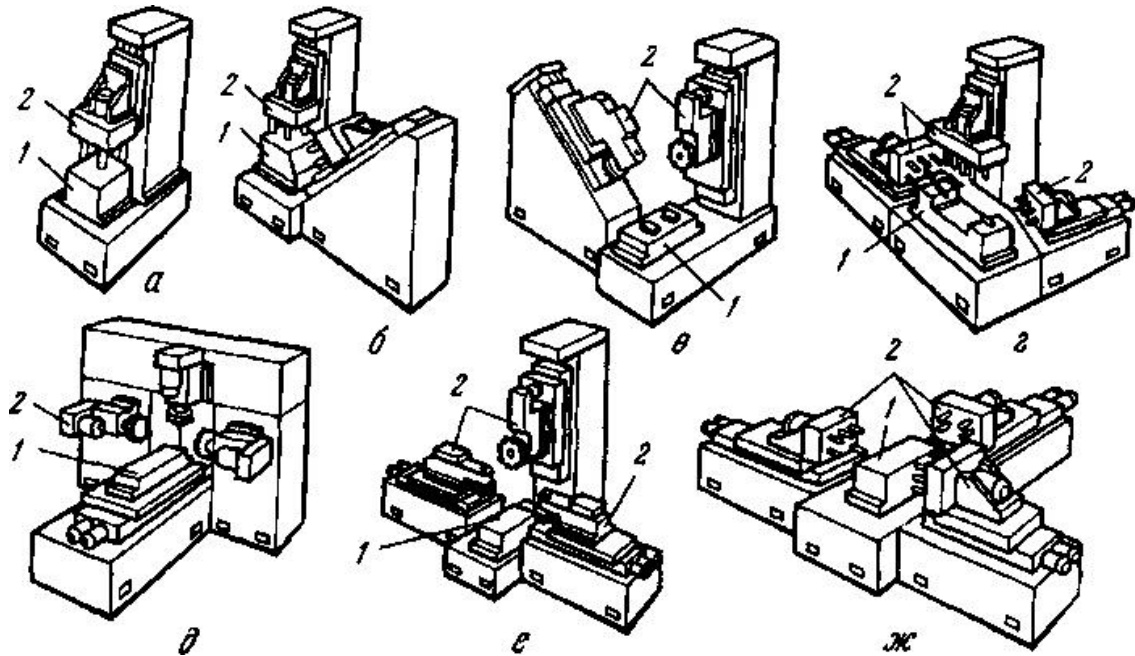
Типові компоновки агрегатних верстатів зі стаціонарними пристосуваннями
